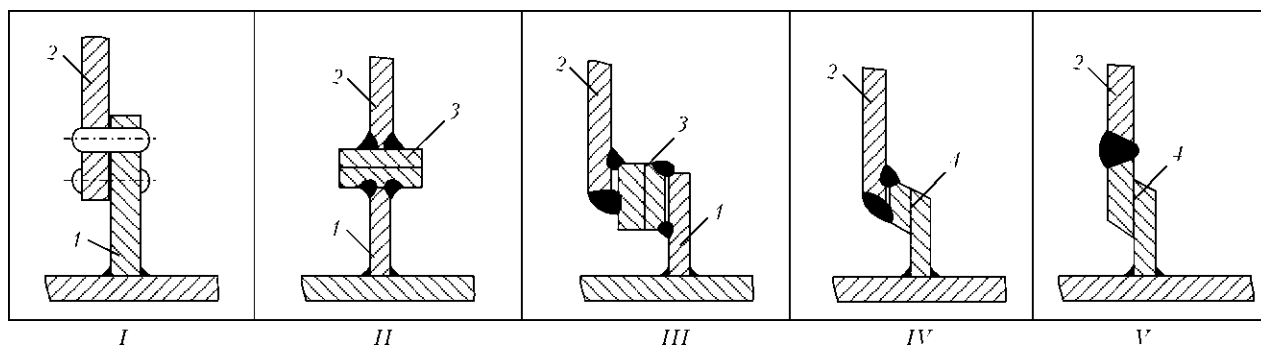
Варианты типовых узлов соединений алюминиевых надстроек со стальным корпусом судна: I — клепаные узлы; II-V — сварные узлы с применением биметалла (II — тавровые; III, IV — нахлесточные; V — стыковые); 1 — стальной комингс; 2 — алюминиевая надстройка; 3 — традиционный биметалл; 4 — комингсный биметалл
